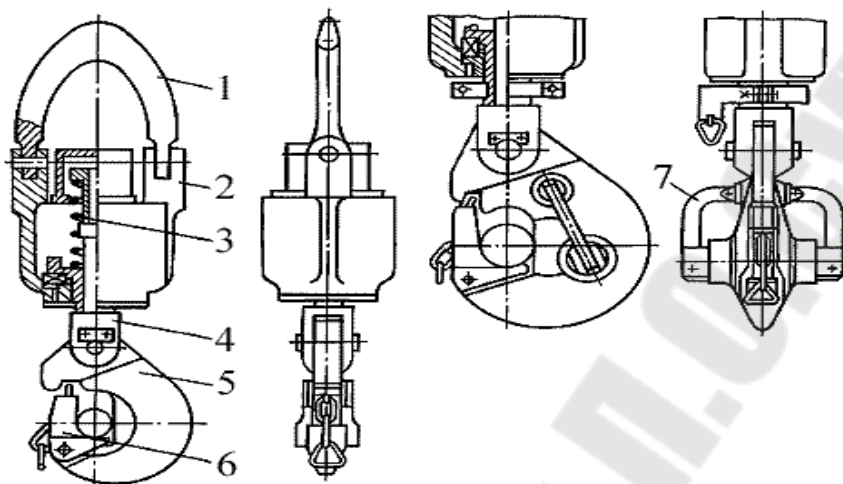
Подъёмные крюки: 1-серьга; 2- корпус; 3- пружина; 4- ствол крюка; 5- собственно крюк; 6-седло; 7- защитные скобы
